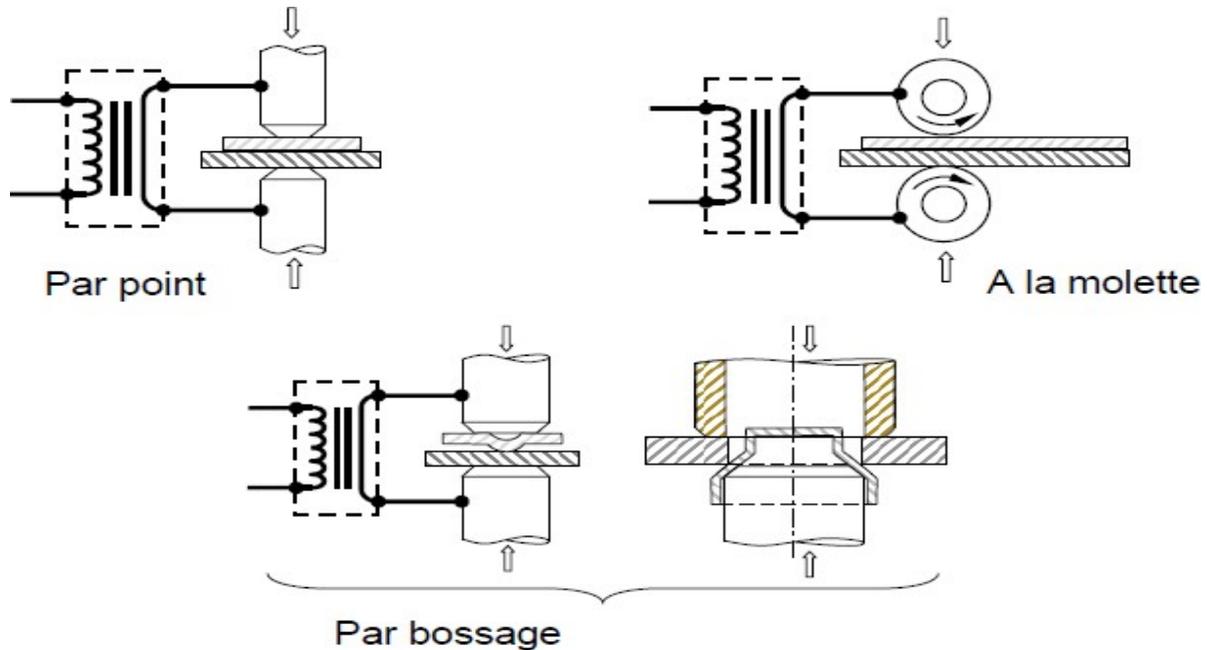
Principaux procédés de soudage par résistance
